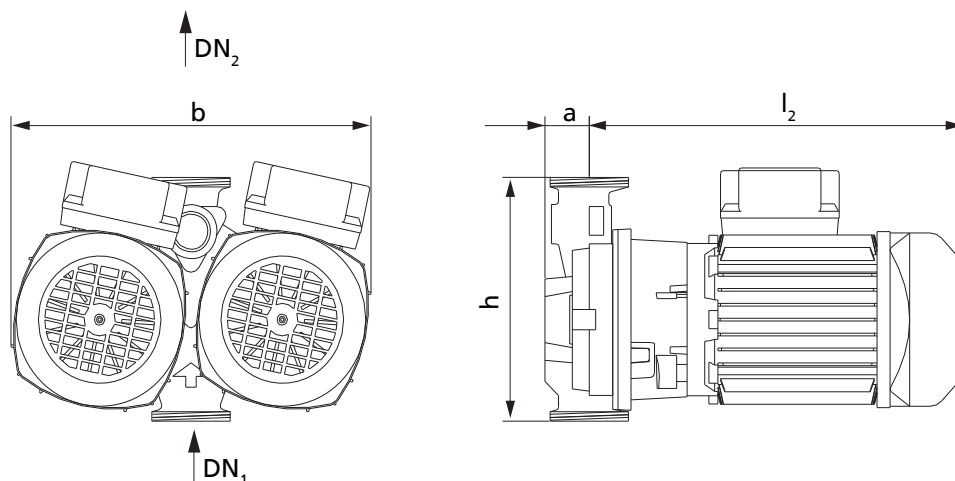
Размеры насосного агрегата с резьбовым соединением, типоразмер 032-032-080
